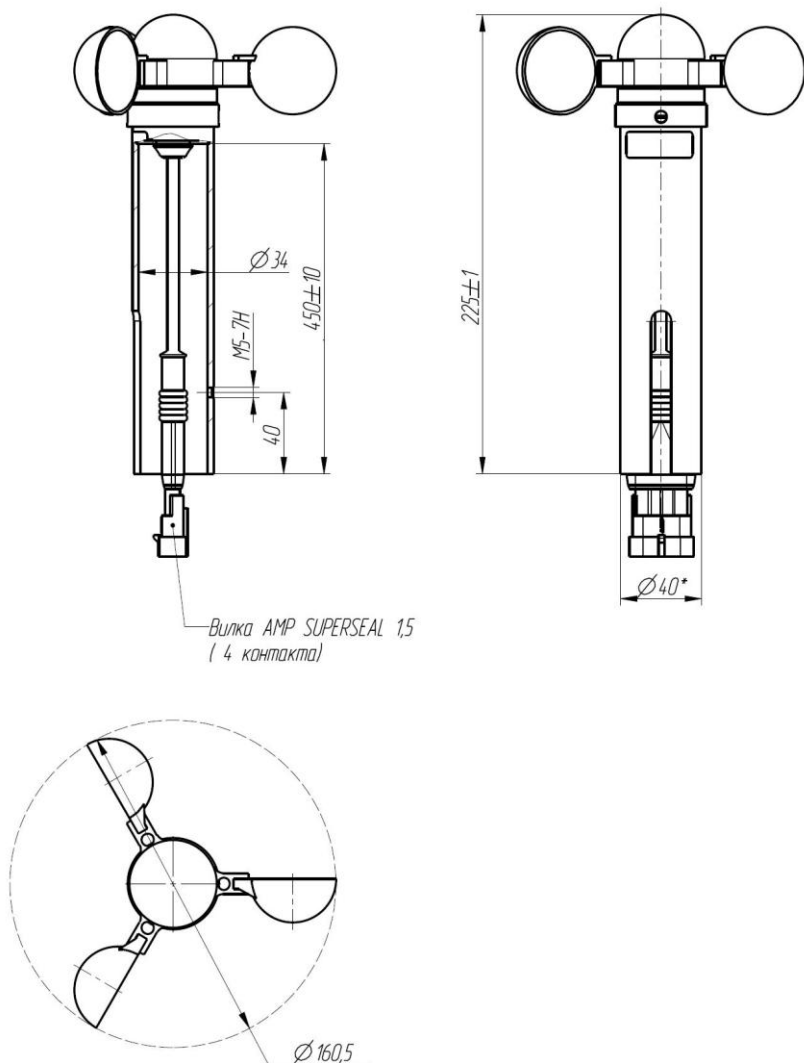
Габаритные и присоединительные размеры ДСВ1.13
